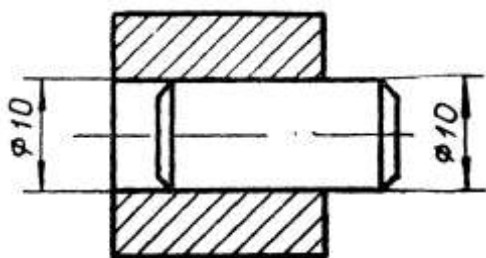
Соединение стержня со втулкой с номинальными размерами
